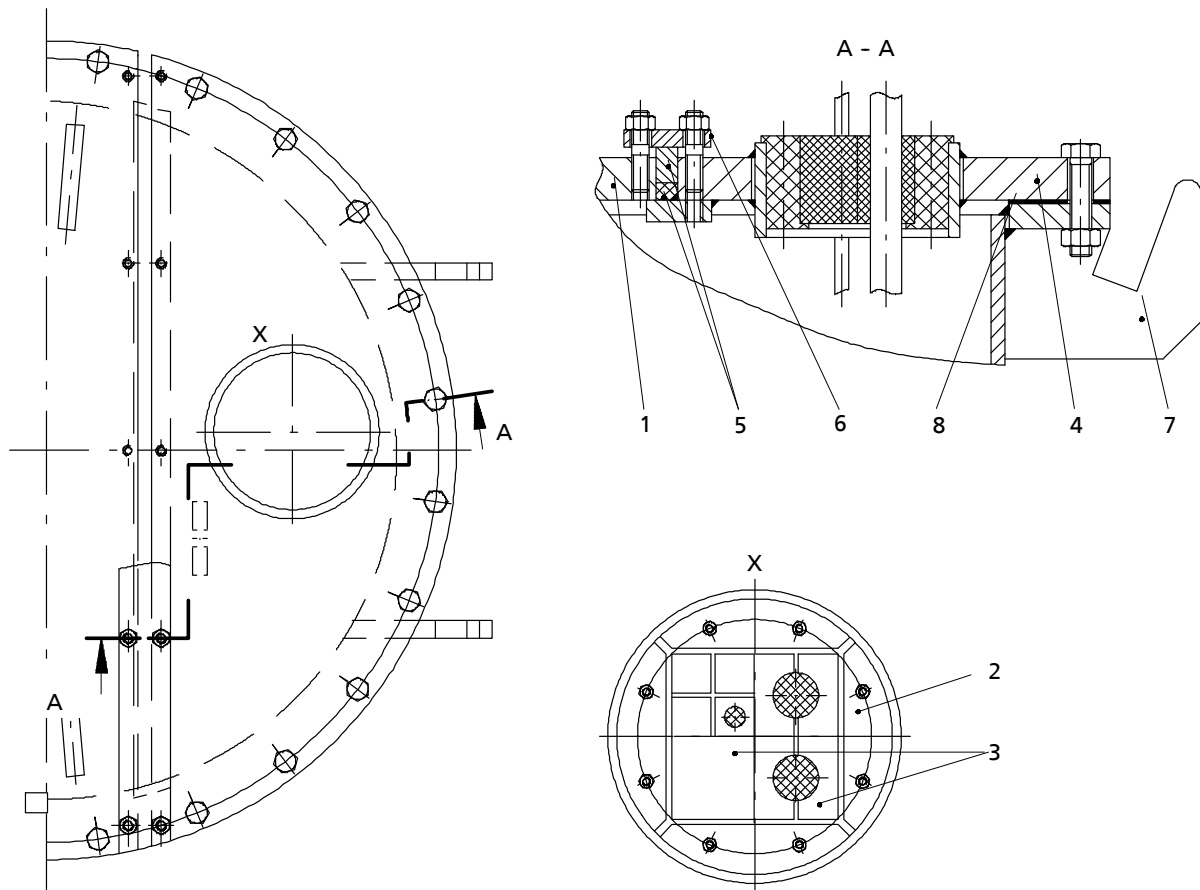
Ausführungsvariante: mit Stoprahmen (bis 1 bar)
